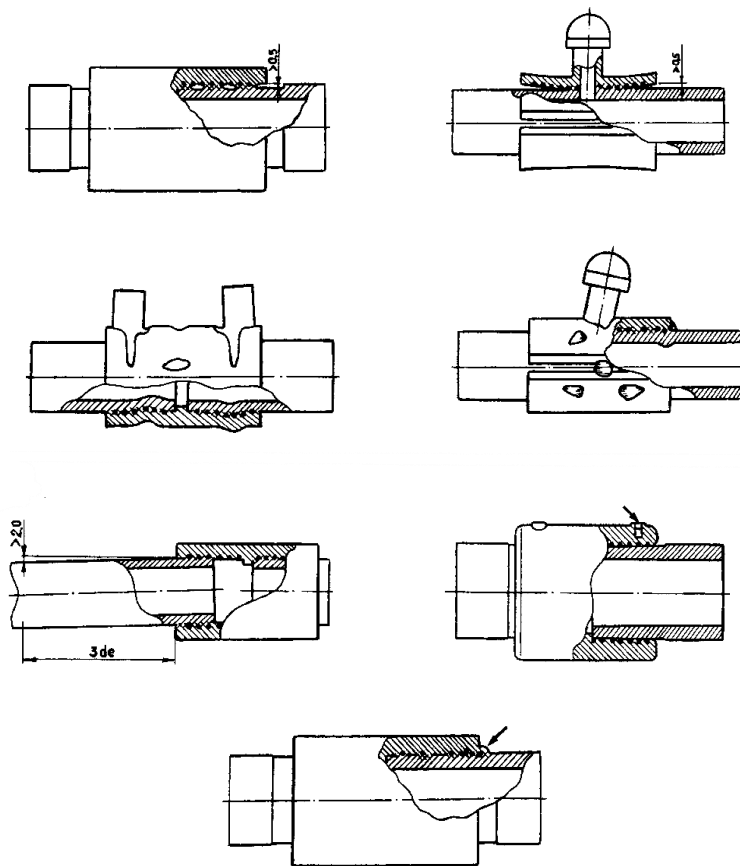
Виды дефектных соединений при сварке деталями с ЗН
